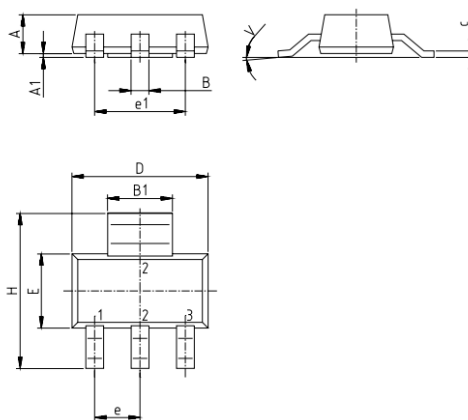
Габаритні розміри лінійного стабілізатора напруги LD1117
